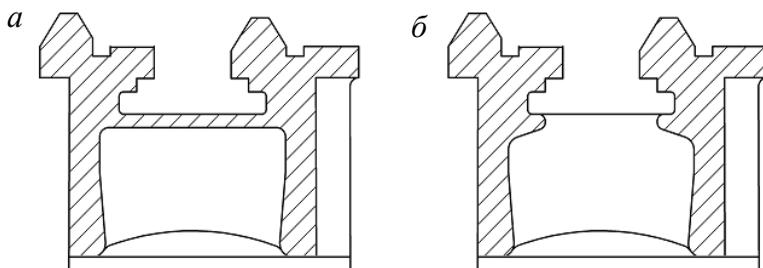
Полуоткрытый (а) и открытый (б) профиль поперечного сечения станины токарно-винторезного станка
